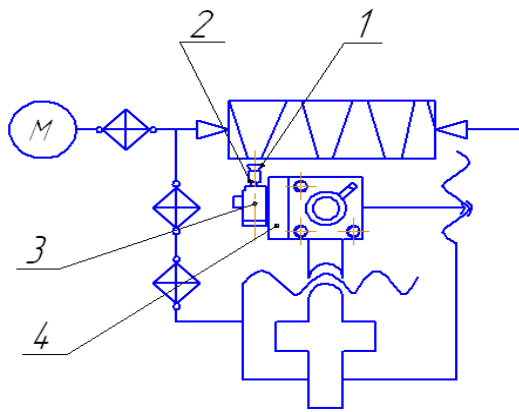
Вариант исполнения инструментального модуля для ротационного точения на станке 16К20: кинематическая схема установки на токарный станок: 1 – твердосплавная пластина; 2 – оправка; 3 – электрошпиндель Э-18/0,63; 4 – кронштейн,
